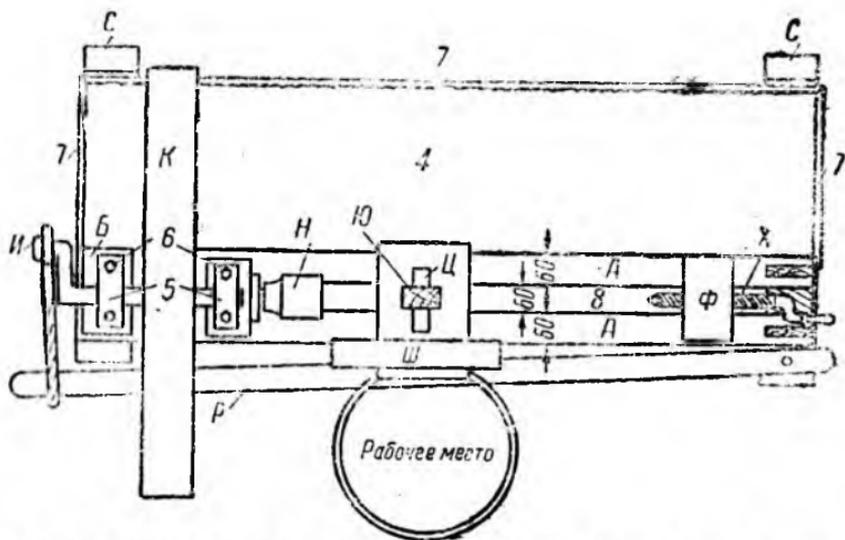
Самодельный универсальный токарный станок (вид сверху)
